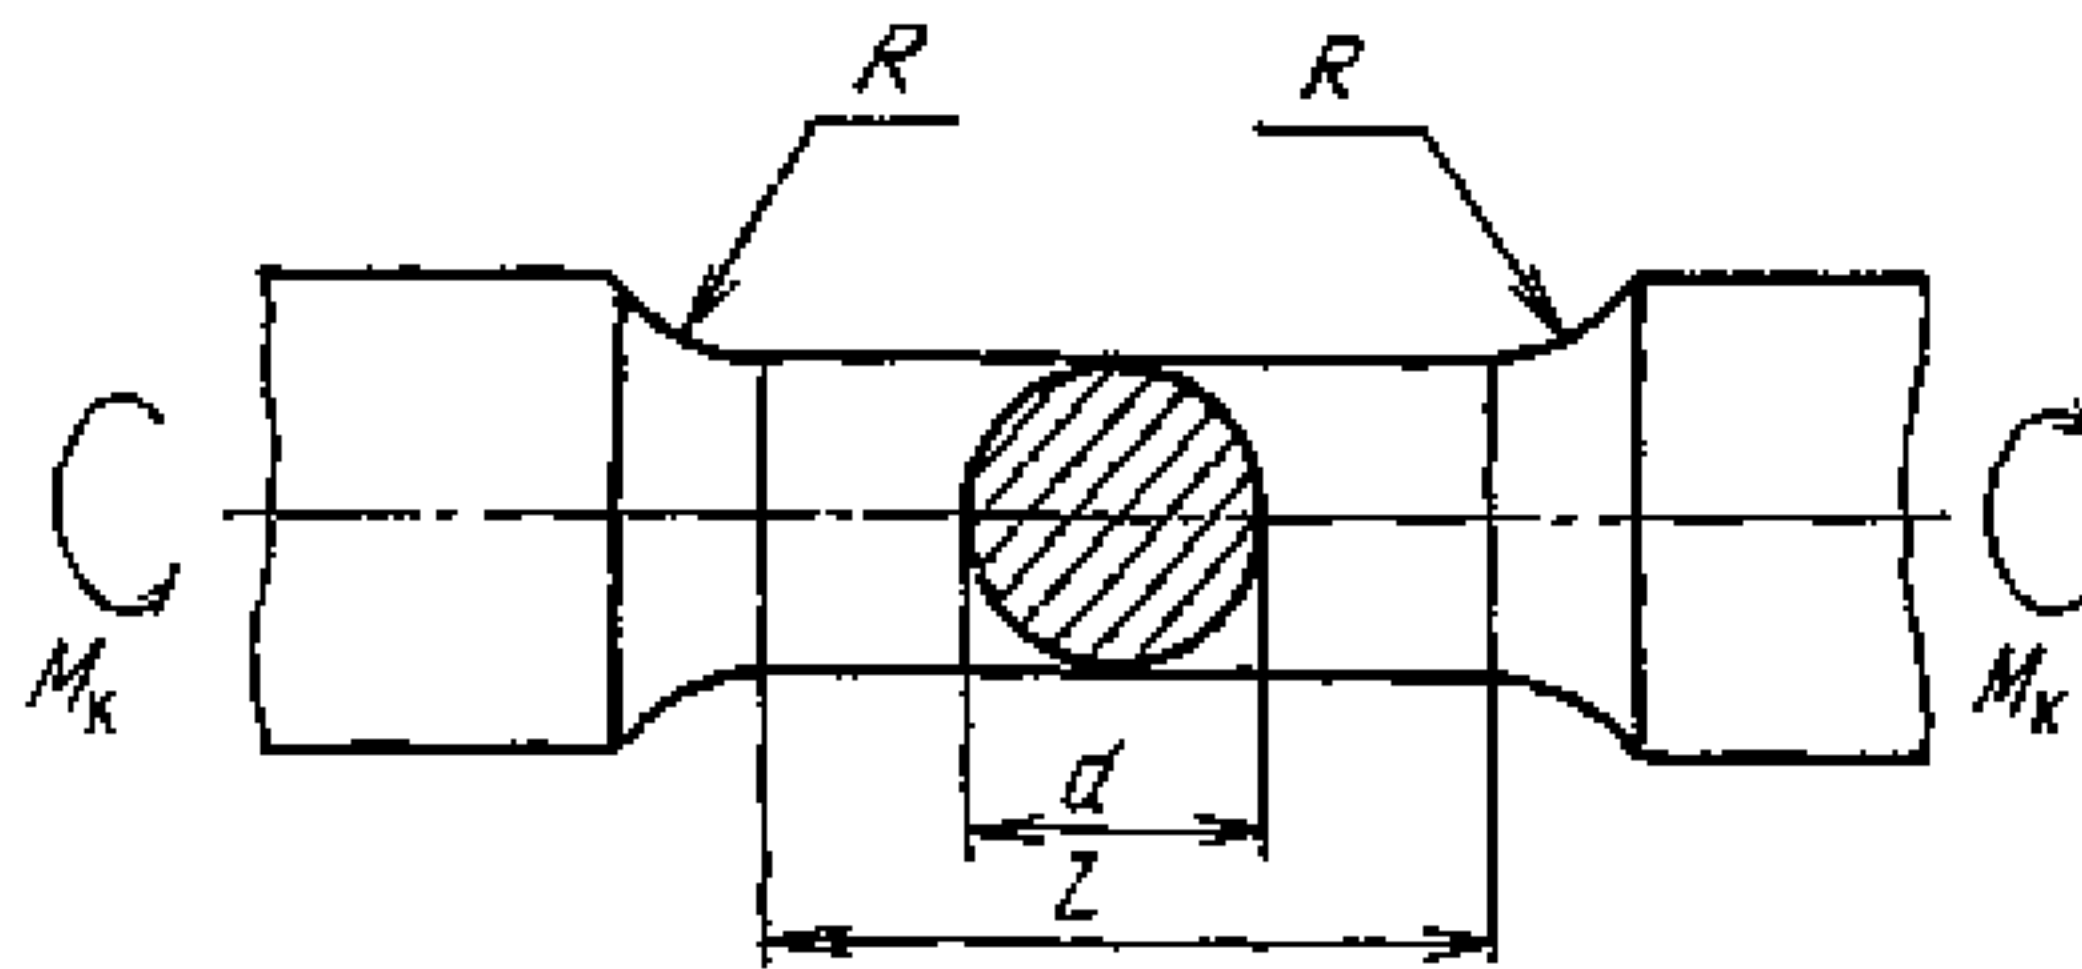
Форма и размеры рабочей части образца для испытаний при повторном кручении:
